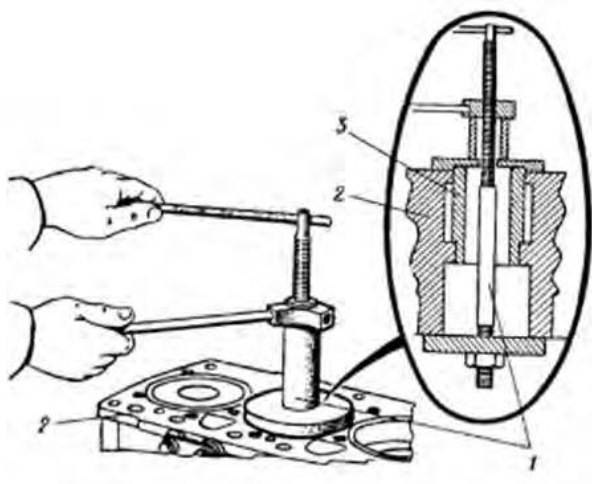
Запрессовка гильзы цилиндра винтовым приспособлением:
